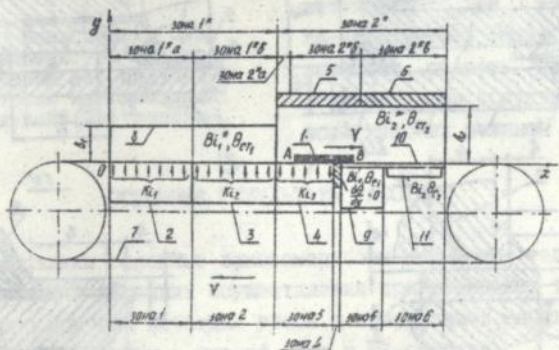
Схема печи для ИК-пайки: 1 - ПУ; 2, 3, 4 - секции предварительного резистивного нагрева; 5, 6 - секции ИК-нагрева; 7 - транспортер; 8 - крышка; 9 - вентилируемый канал; 10 - крышка стола печи; 11 - оребренная поверхность.
